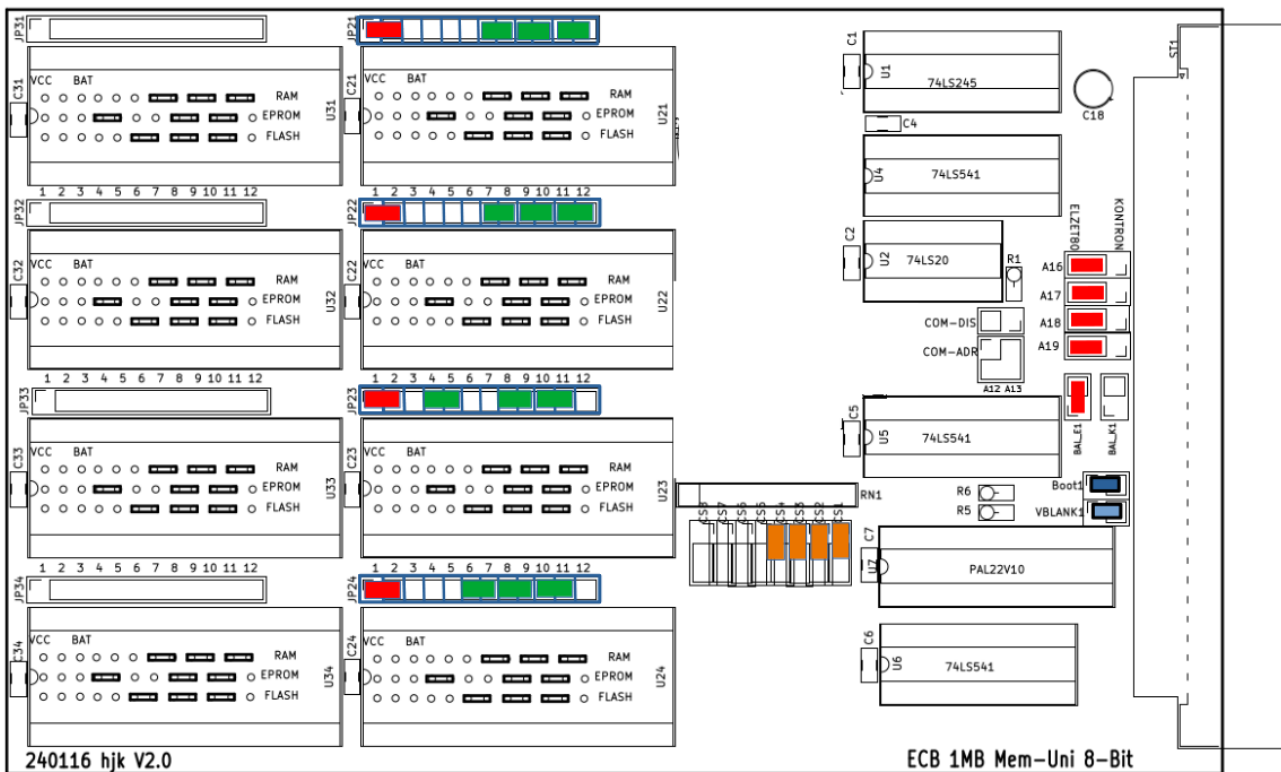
Beispiel Bestückung mit 4 Speichern ohne Akkupufferung
